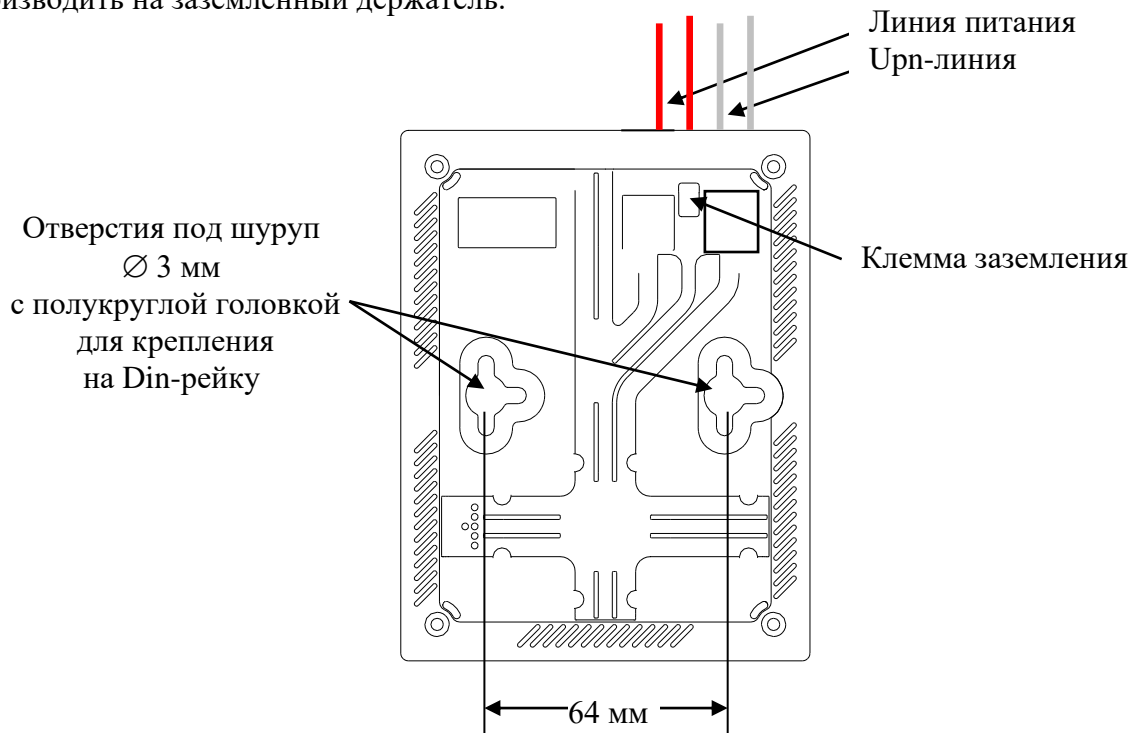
Присоединительные размеры базовой станции BC7-UPN-i1a/i2b (вид сзади)
